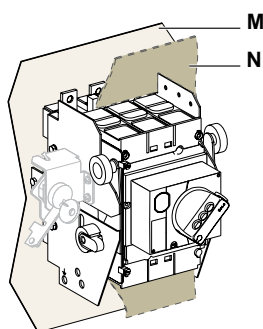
Габаритные и установочные размеры втычных и выдвжных выключателей ВА40-02, ВА40-06 с ручным приводом с поворотной рукояткой.
